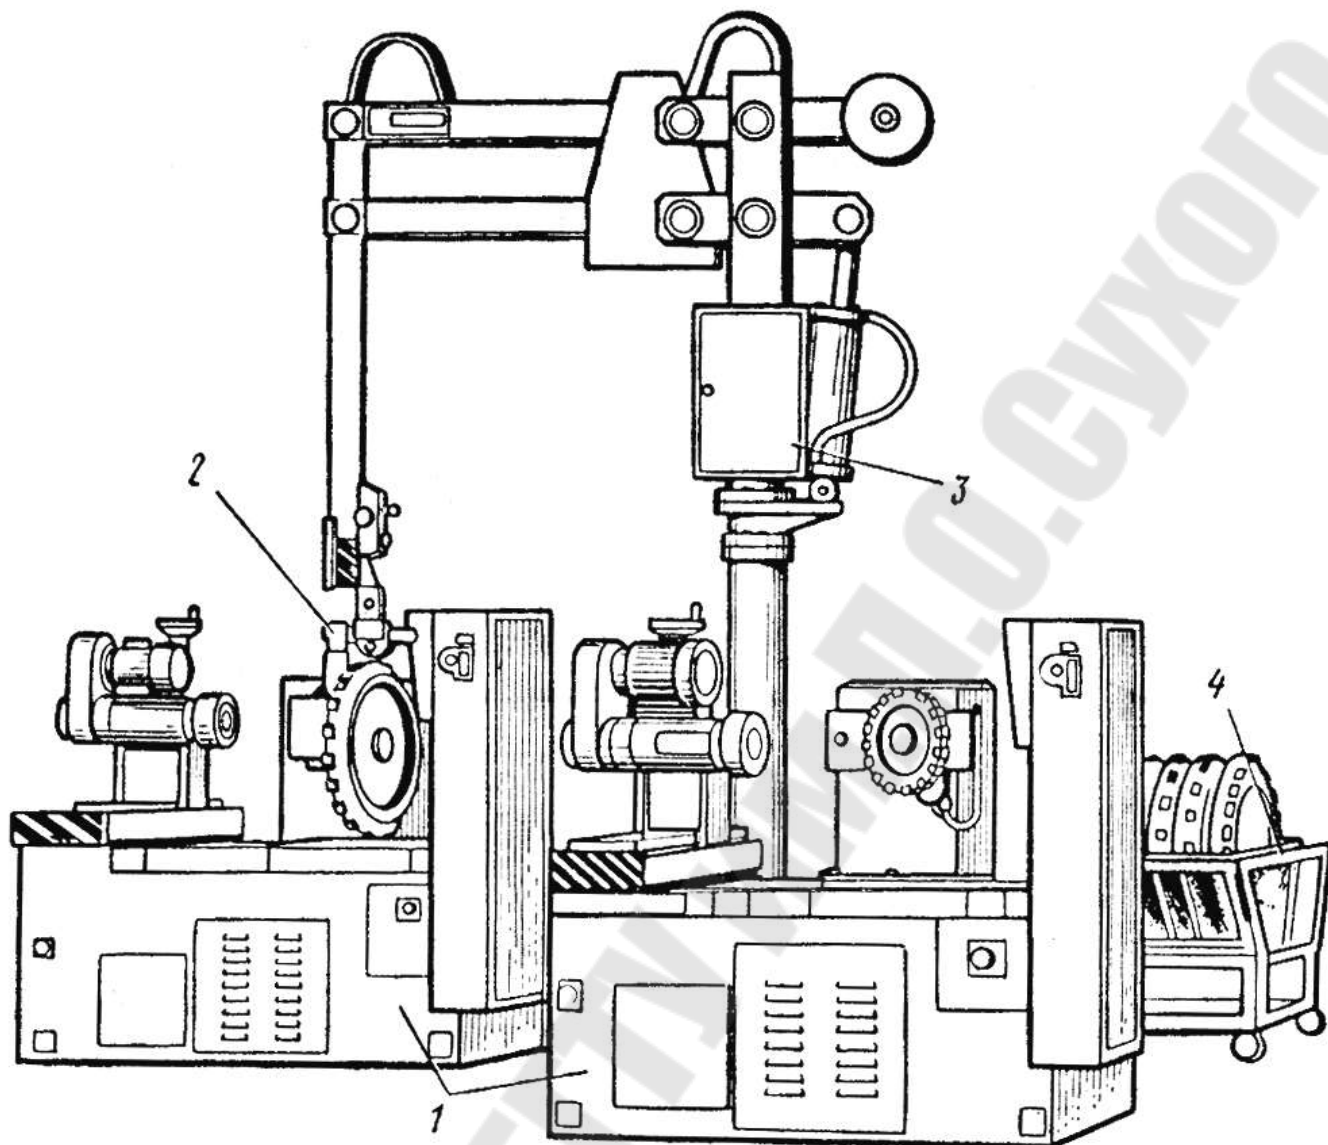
Общий вид заточного комплекса ВЗ-219К для заточки торцовых фрез: 1 – полуавтомат модели ЗБ667Ф2; 2 – схват; 3 – манипулятор; 4 – накопитель
